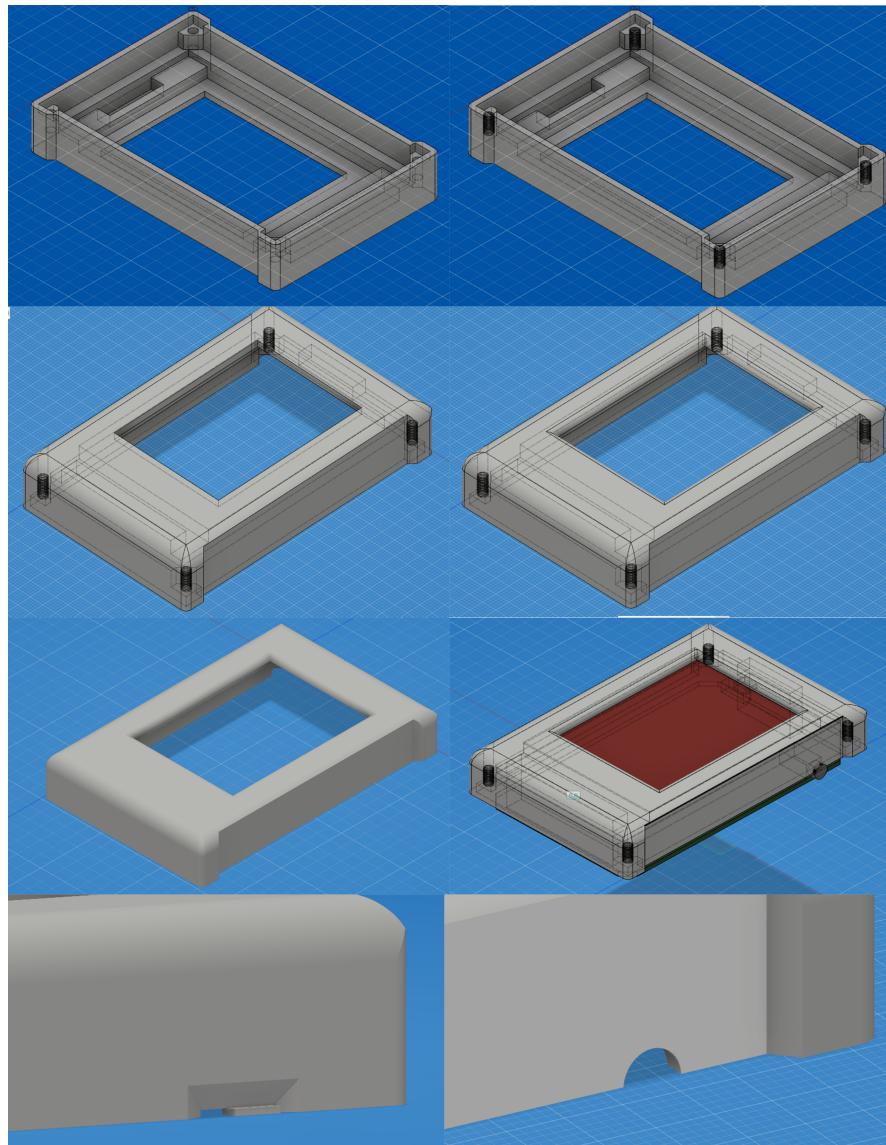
Proceso del Diseño del Molde Superior Parte 1
